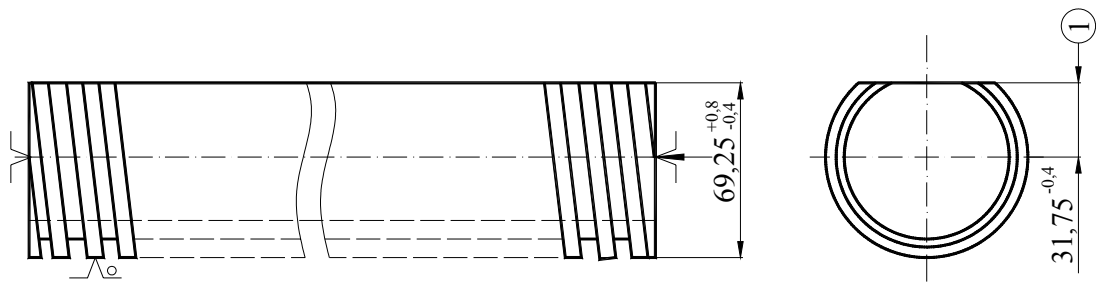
Ескіз фрезерування заготовок стопорних кілець з Г-подібним профілем
